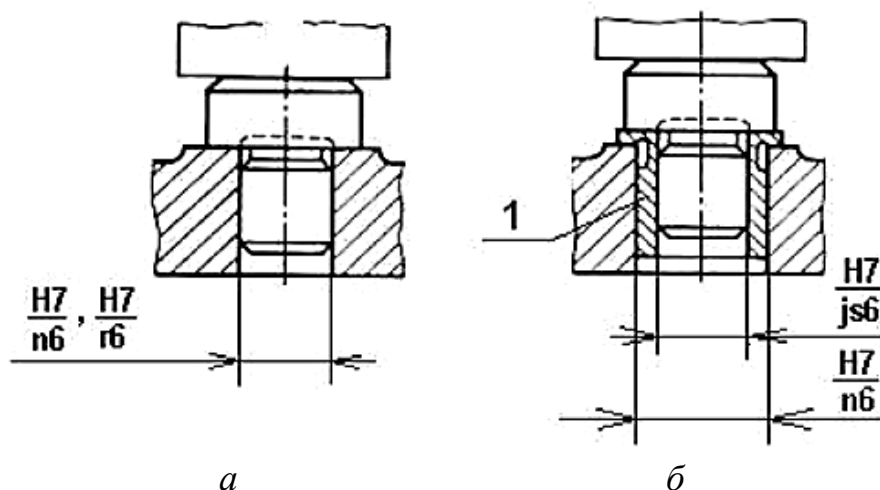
Варианты установки точечных опор в корпусе приспособления:
